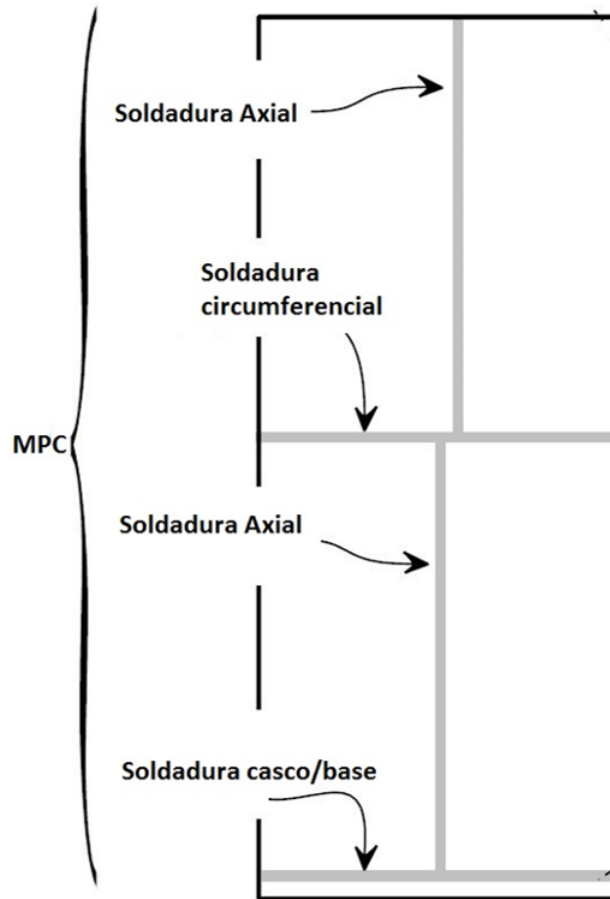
Soldaduras del casco del MPC. Fuente: [5]
